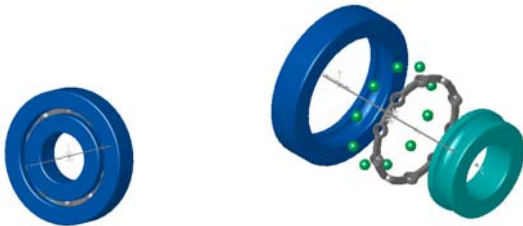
深沟球滚动轴承的装配体模型与爆炸视图
